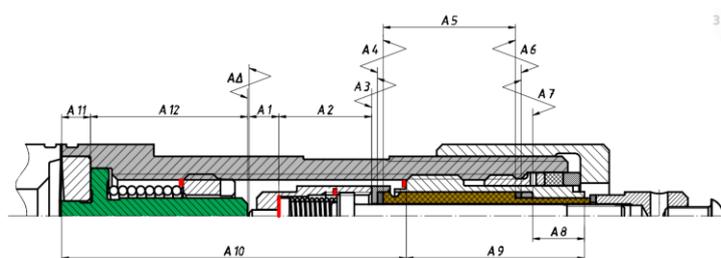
Схема размерной цепи А, обеспечивающей при сборке достижение точности зазора между исполнительными поверхностями СП
